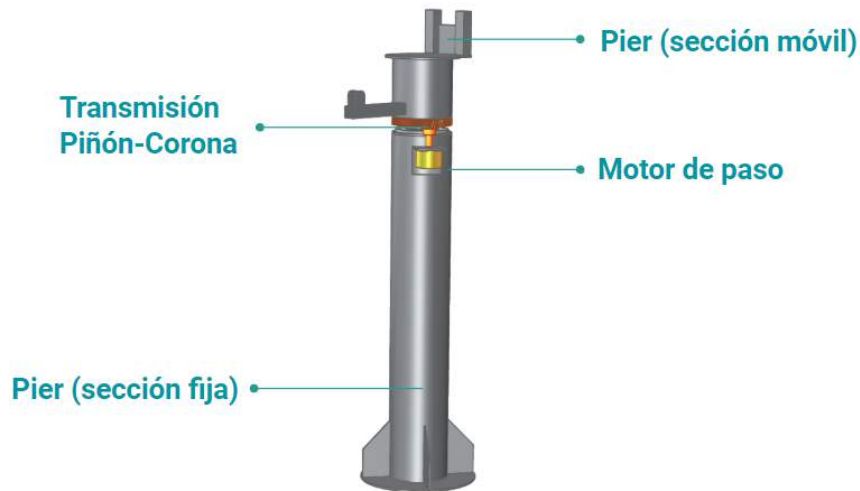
Diseño CAD de sistema de rotación en azimut.
